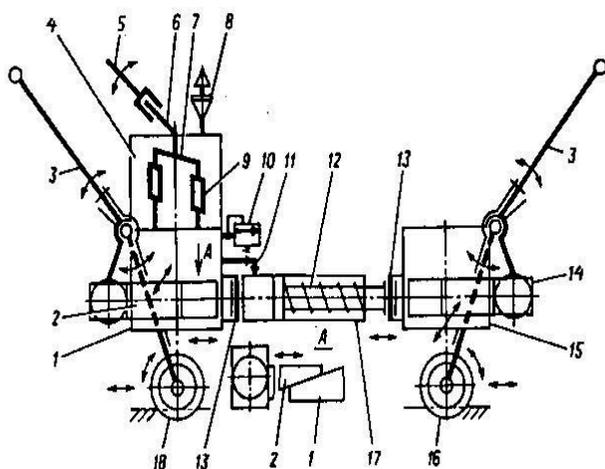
Структурная схема разгонщика РН-04: *1, 15* – корпуса; *2, 14* – клинья; *3* – ручка; *4* – масляный бачок; *5* – рабочая съемная рукоять; *6* – вал; *7* – коромысло; *8* – сетчатый фильтр; *9* – плунжерная пара; *10* – аварийный клапан; *11* – шланг; *12* – возвратная пружина; *13* – ось; *16, 18* – ролики; *17* – гидроцилиндр
